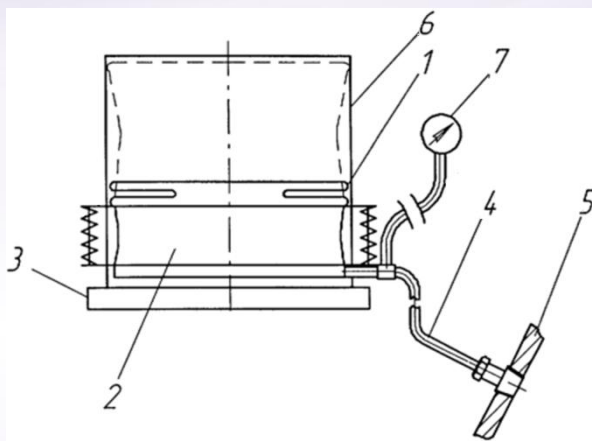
Уравновешивающее устройство: 1-эластичный баллон, 2-полость компенсирующая разрежения, 3-рама, 4-трубопровод, 5-корпус редуктора, 6-защитный колпак, 7-манометр.
